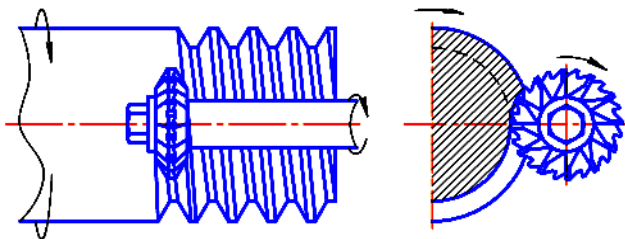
Схема фрезерования наружной резьбы дисковой профильной фрезой
